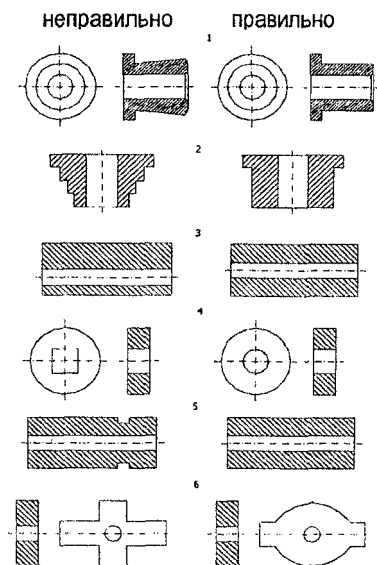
Примеры конструирования металлокерамических заготовок
